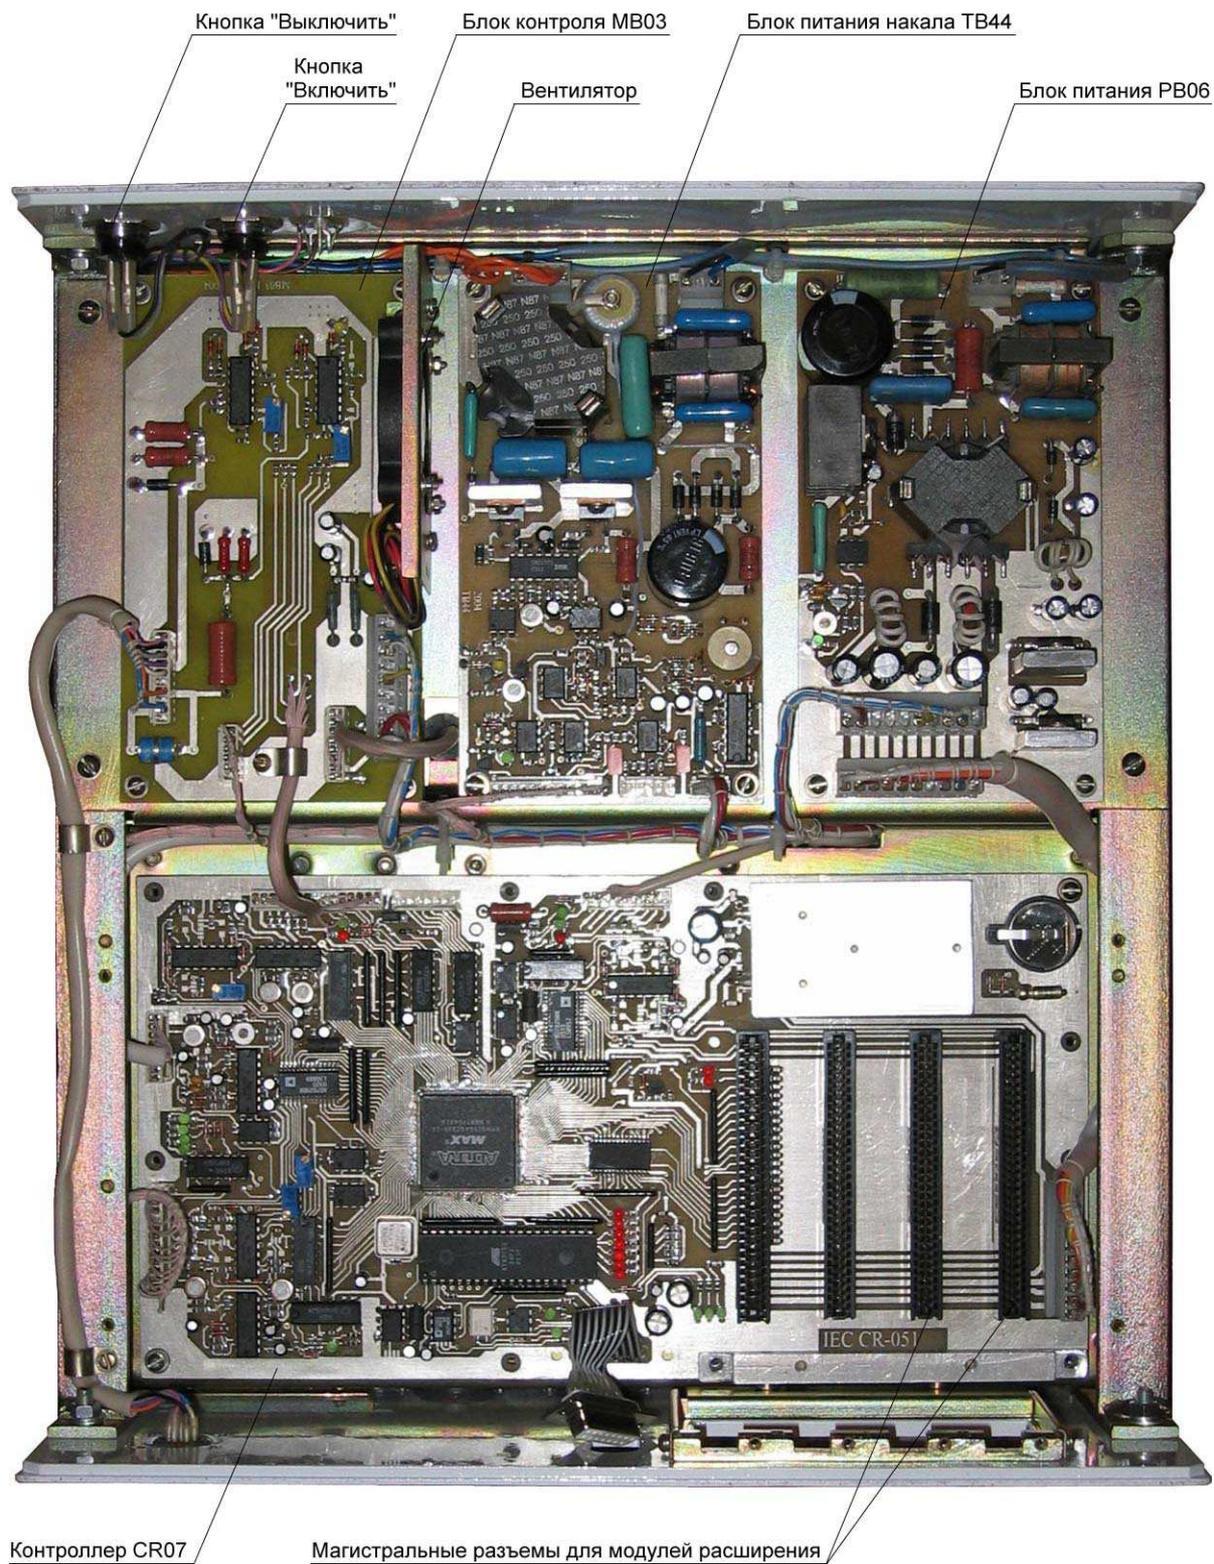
Блок управления IEC-F6 со снятыми крышками кожуха. Вид сверху
